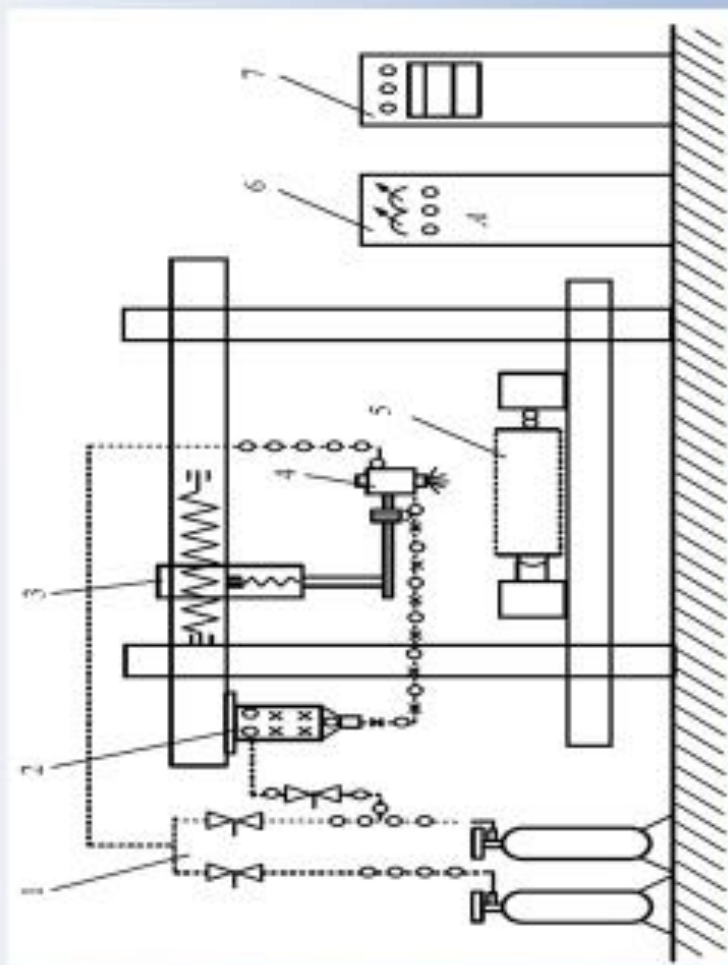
Принципова схема установки плазмового напшення УПУ-3Д
